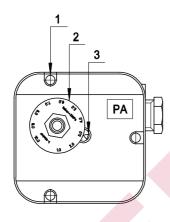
1-В инт-заглушка 2-Регулировочная гайка 3-Указатель регулировки
